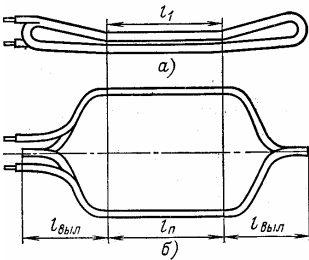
Катушка двухслойной обмотки статора. Общий вид
